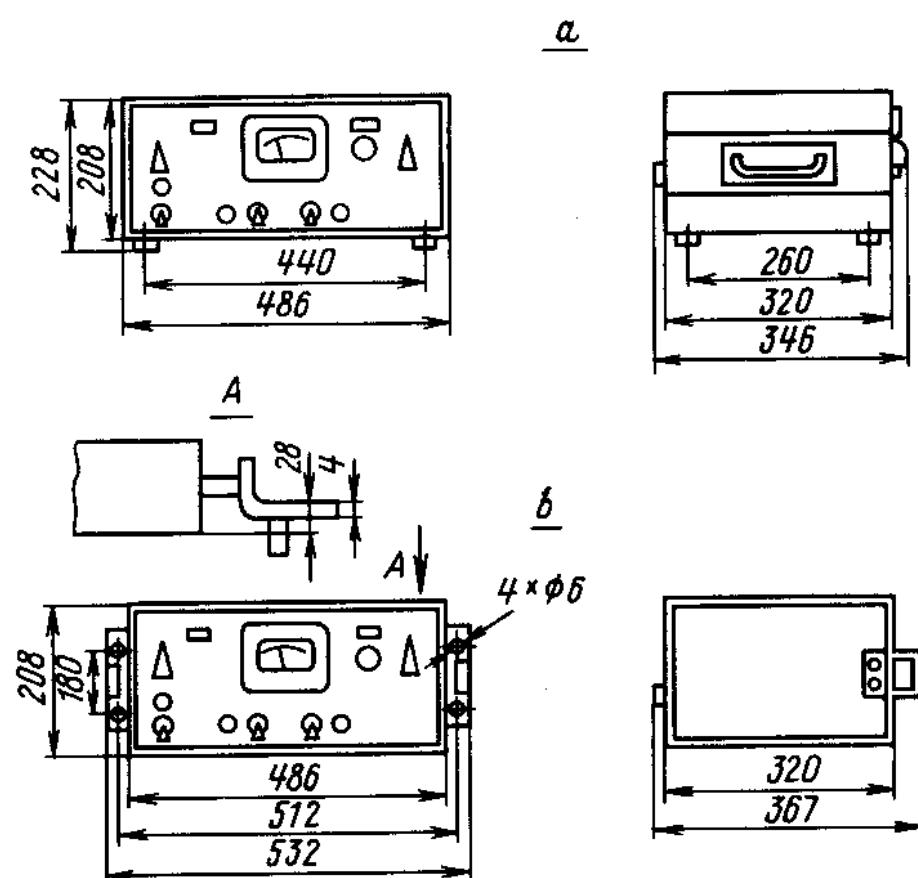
Габаритные размеры измерительного блока вакуумметра ВИ-14:
